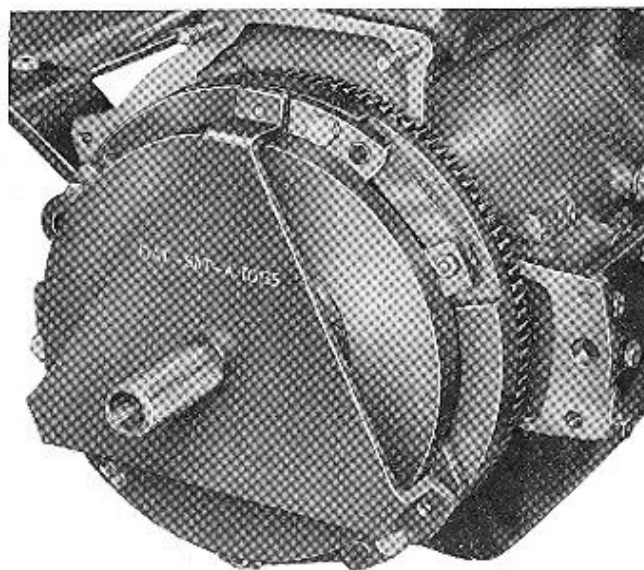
Zentrierung der Scheibenfeder und der Kupplungs-scheibe mittels des Werkzeugs A. 70135 während des Festziehens der Befestigungsschrauben.
